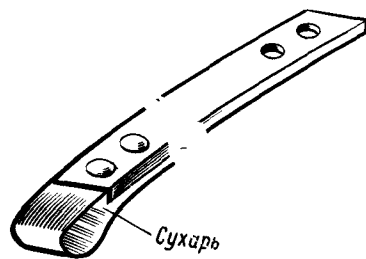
Стальной блокировочный контакт с наклепанным сухарем
